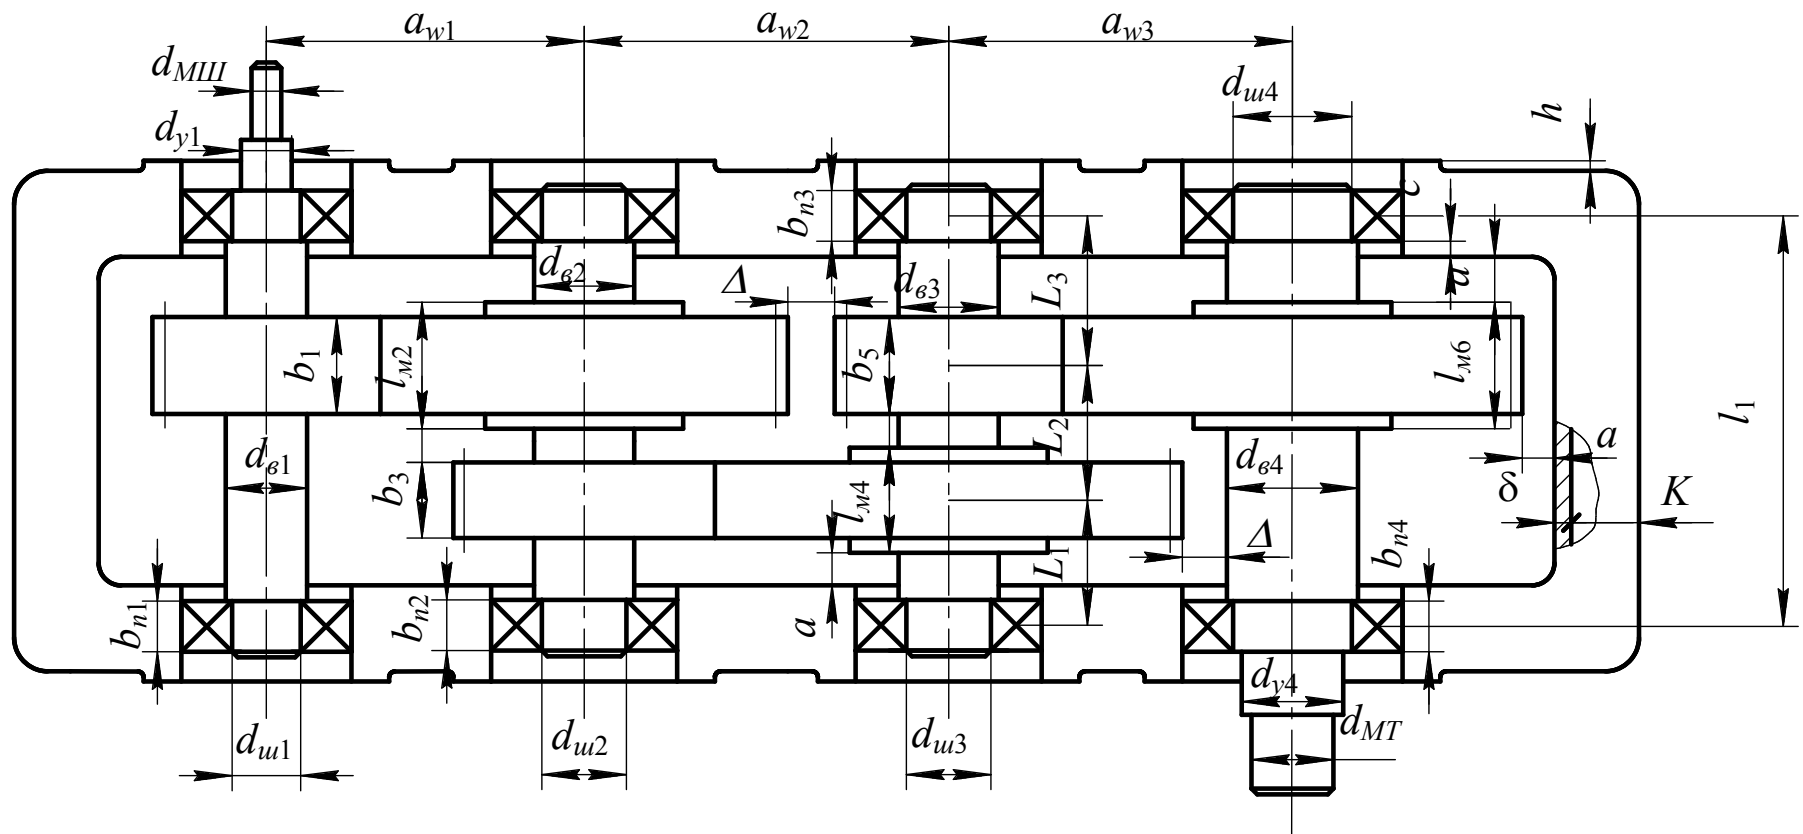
Эскизная компоновка трехступенчатого цилиндрического редуктора
